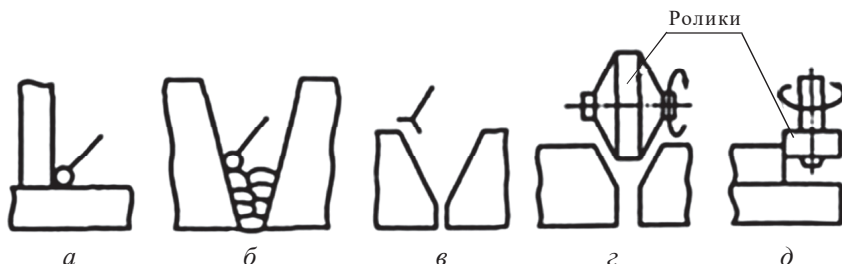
Контактные датчики сварочного инструмента:
